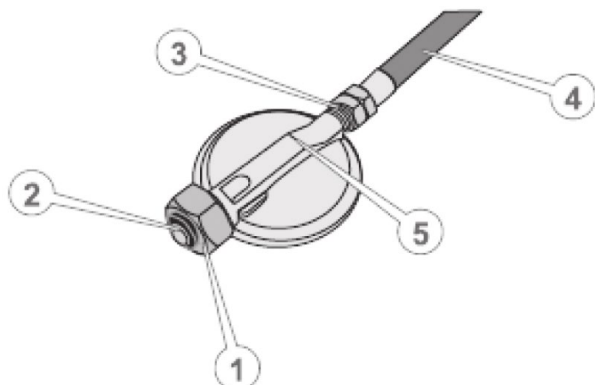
Загальний вигляд газового редуктора (редуктора тиску), під'єднаного до газового рукава.
